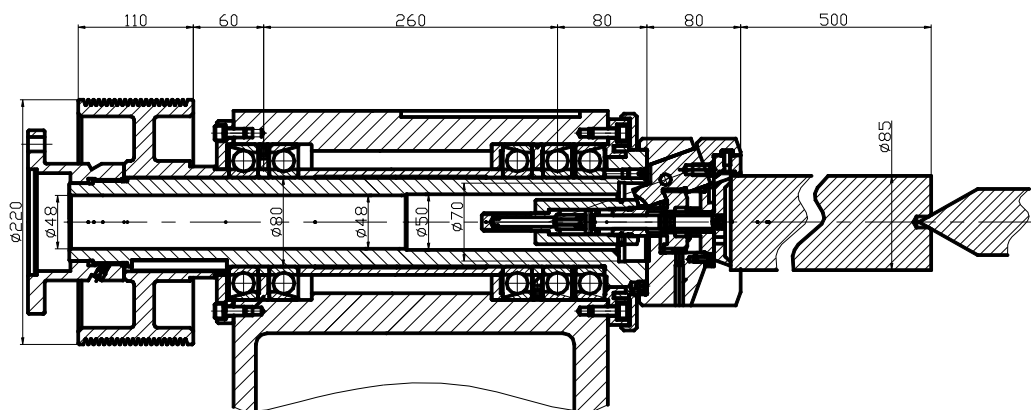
Конструктивна схема шпиндельного вузла верстата мод. ПАБ-130
